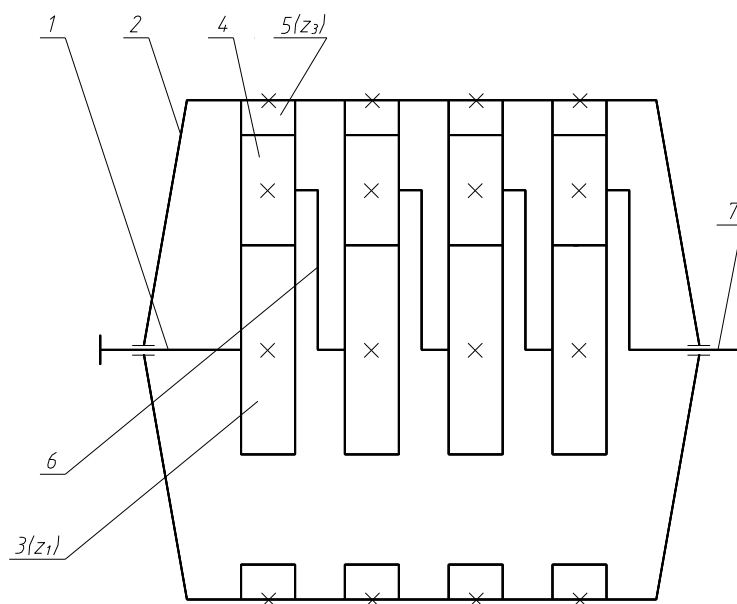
Кинематическая схема планетарной передачи типа 2К-Н, с наружными и внутренними зацеплениями: 1 – входной вал; 2 – корпус; 3 – центральное колесо с наружными зубьями; 4 – сателлит; 5 – колесо с внутренними зубьями; 6 – водило; 7 – выходной вал передачи
